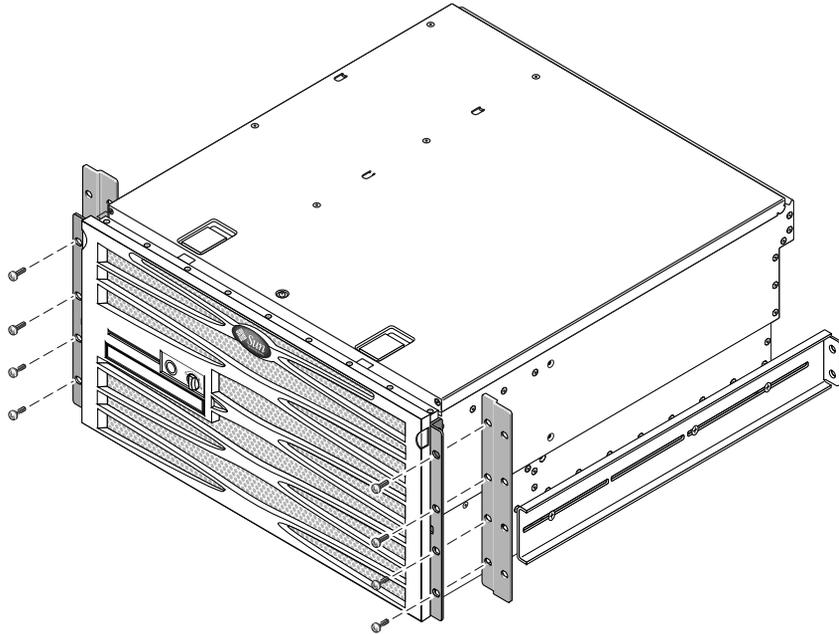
Montaje de los soportes de ajuste de 600 mm en los soportes de montaje fijo frontales
